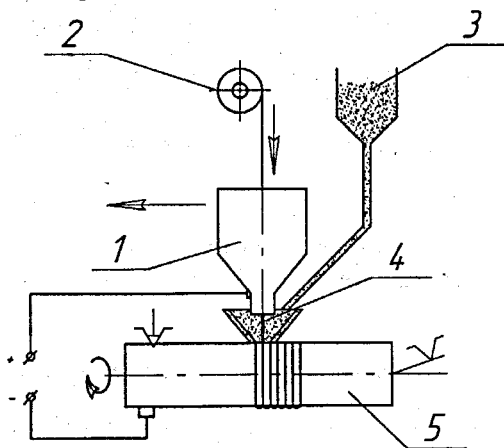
Принципова схема автоматичного електродугового наплавлення деталей під флюсом: 1 — наплавлювальний апарат; 2 — касета з дротом; 3 — бункер із флюсом; 4 — електродний дріт; 5 — наплавлювана деталь
